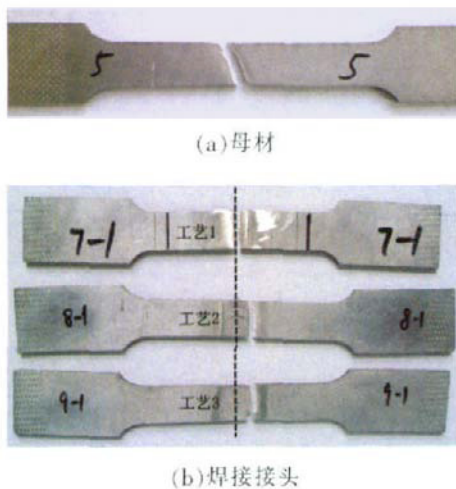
5A06 母材及焊接接头拉伸外观
